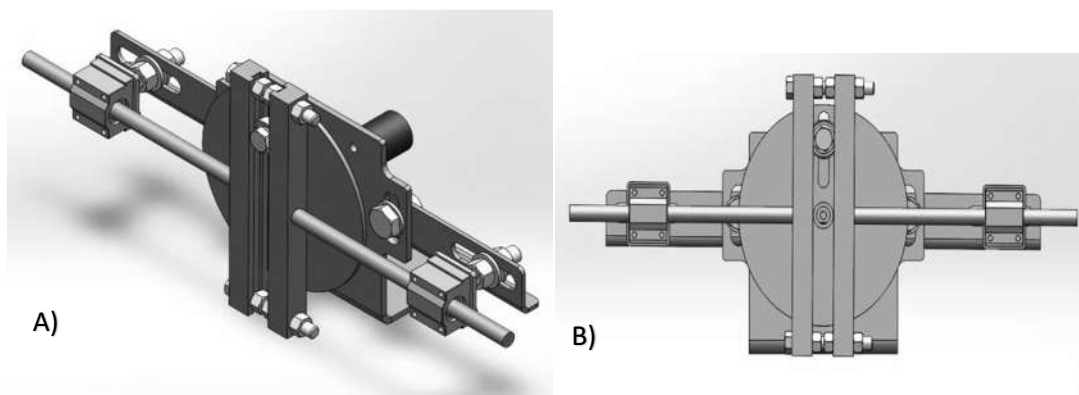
A) Vista isométrica. B) Vista frontal, del módulo para pruebas de fatiga.
